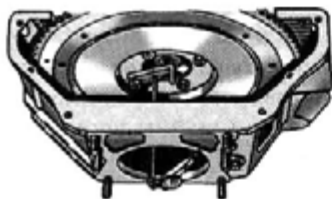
Проверка перпендикулярности заднего торца картера сцепления к оси коленчатого вала
